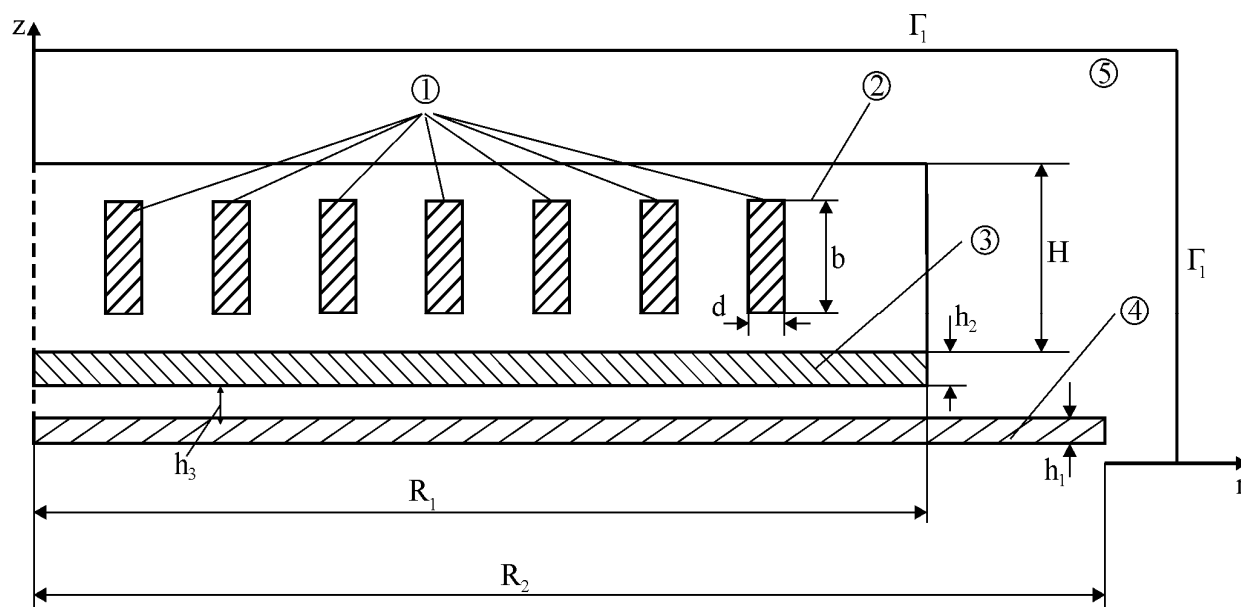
Розрахункова схема складеного багатовиткового індуктора із допоміжним екраном та заготовки: 1 – багатовитковий струмопровід; 2 – допоміжний екран; 3 – діелектричний бандаж; 4 – заготовка
